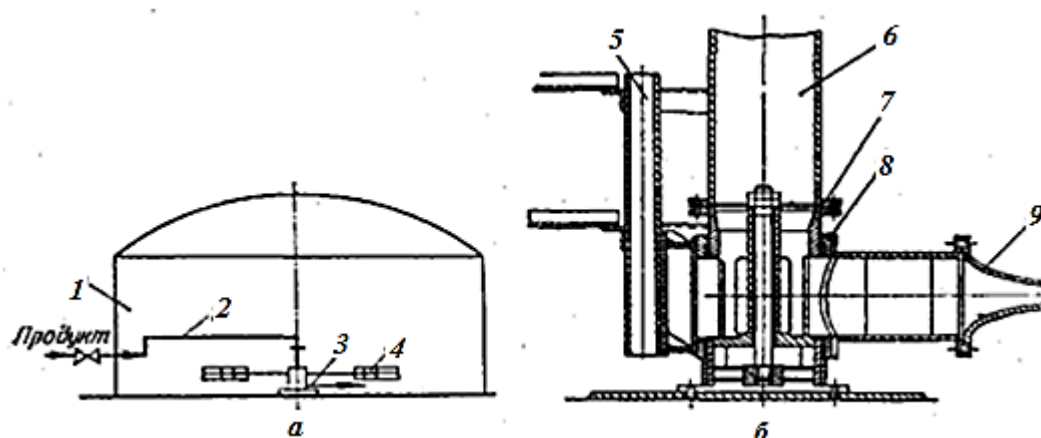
Размещение размывочного устройства в резервуаре (а) и разрезе вращающегося сопла (б): 1- корпус резервуара; 2- подводный трубопровод; 3- вращающееся сопло; 4- лопасти тормозного устройства; 5-крепление тормозного устройства; 6-подводный трубопровод; 7-неподвижная стойка; 8-вращающаяся обойма; 9- сопло.
